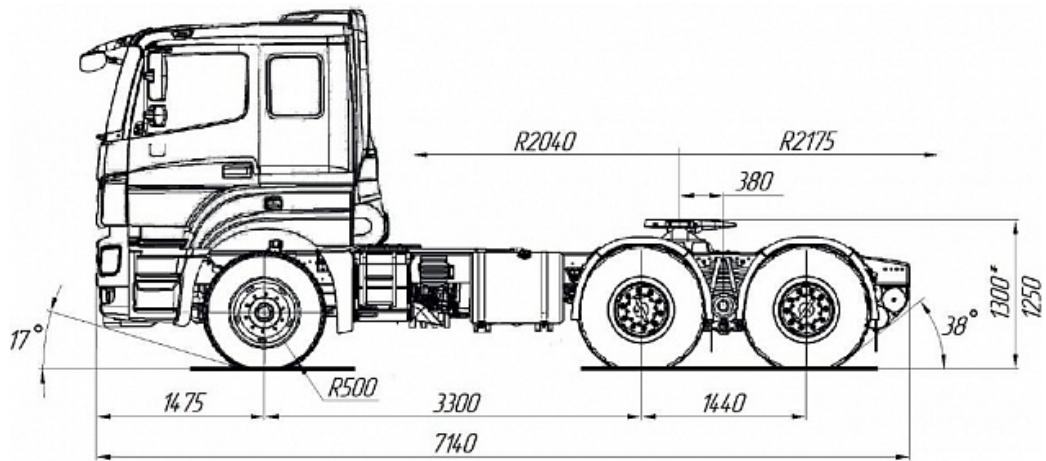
Размеры автомобиля КАМАЗ 65806
